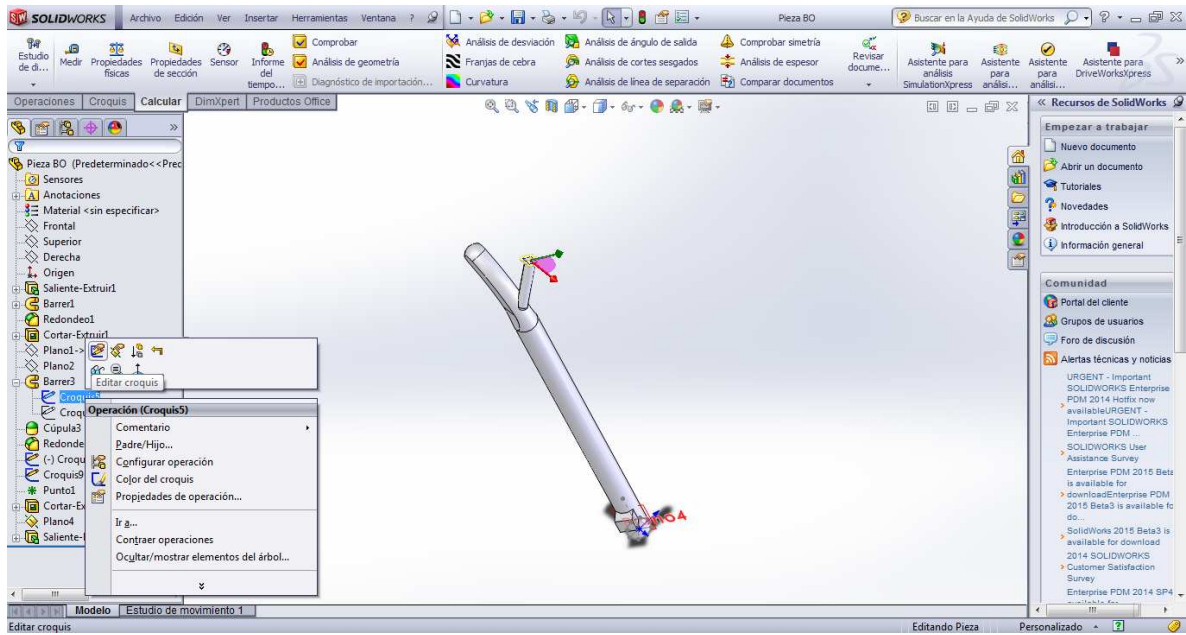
Edición de croquis para modificar la varilla soldada del modelo
